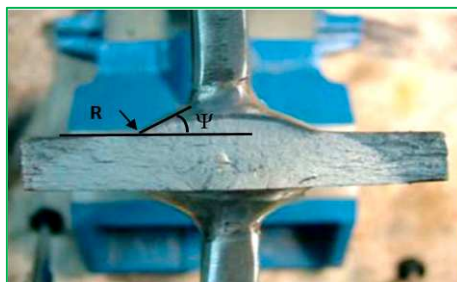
Paramètres géométriques d'un joint soudé [92]
